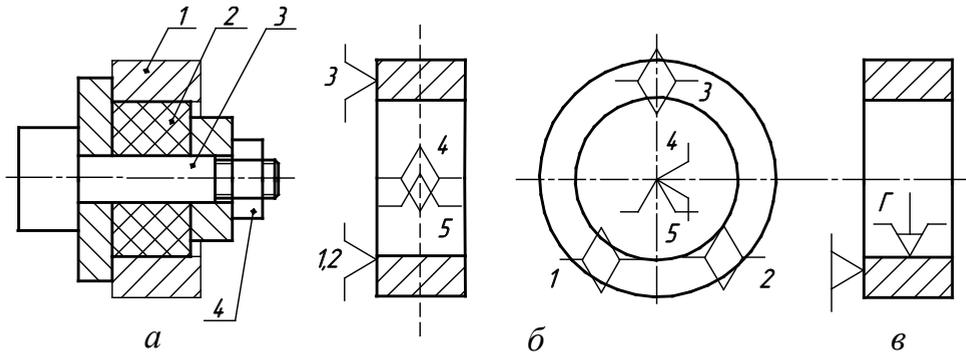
Установка короткой втулки на гидропластовой оправке без зазора:
